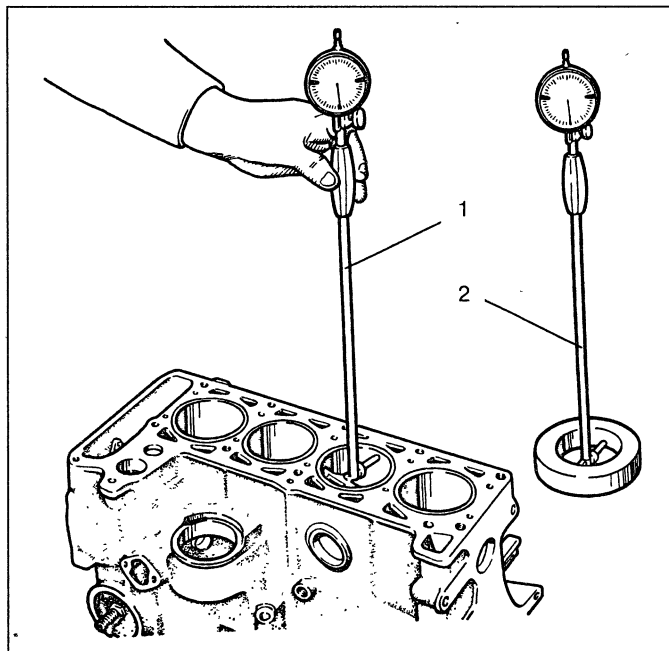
Измерение цилиндров нутромером: 1 – нутромер; 2 – установка нутромера на ноль по калибру
